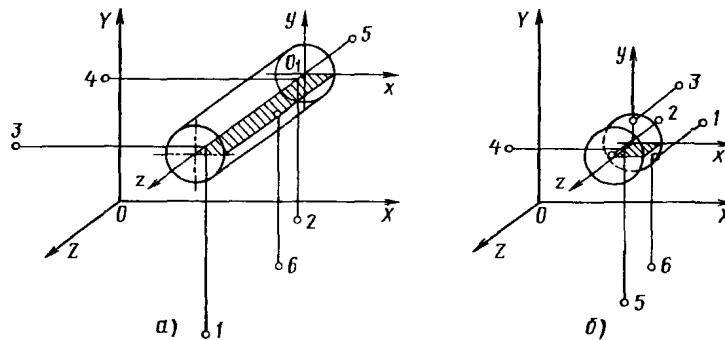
Схемы базирования деталей типа тел вращения: *а* - вал; *б* - диск
